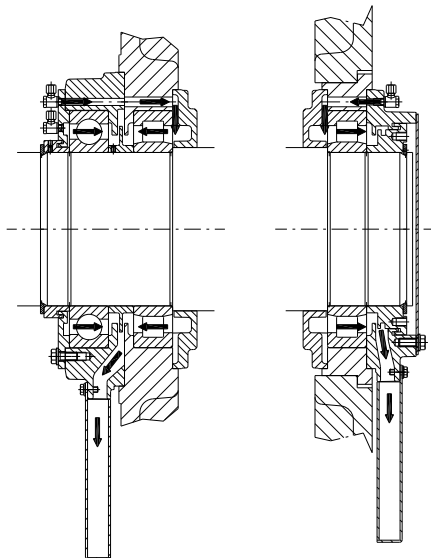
Пример смазочного канала, проходящего через подшипниковый узел горизонтальной машины
